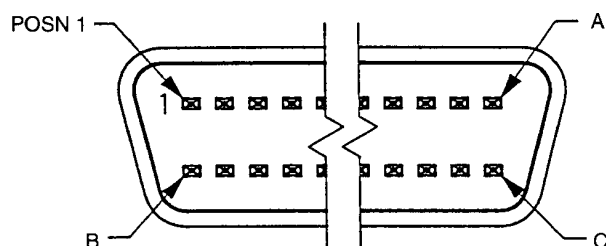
Face d'accouplement d'un connecteur avec contacts mâles
